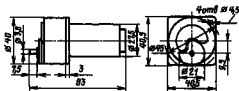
38. Габаритные и установочные размеры двигателей ДКИР-0,4-15, ДКИР-0,4-33
